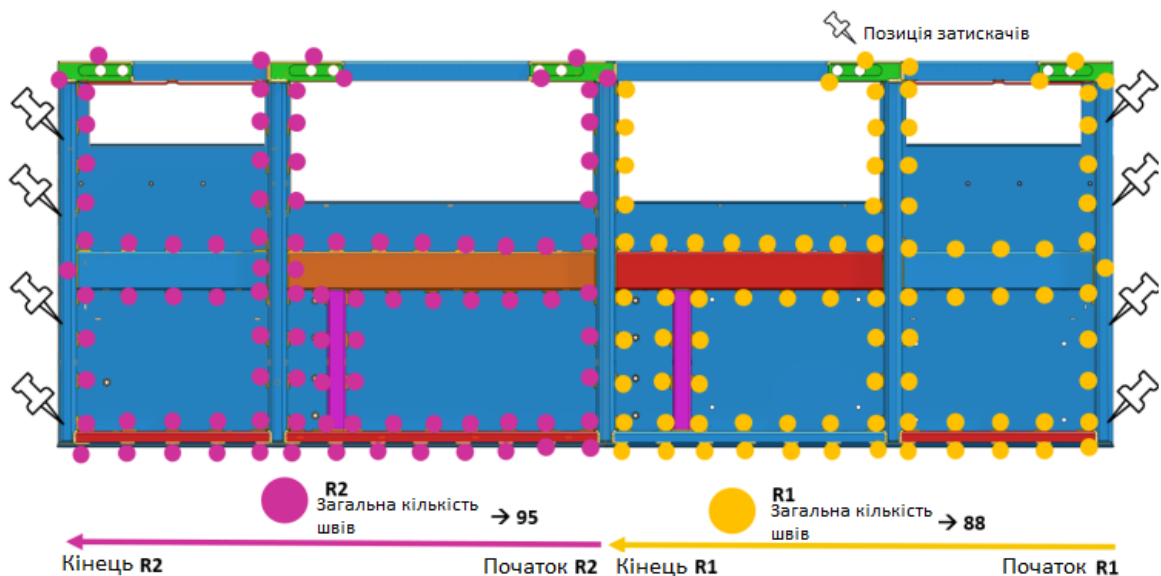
Зварювальною коміркою для зварювання рами
